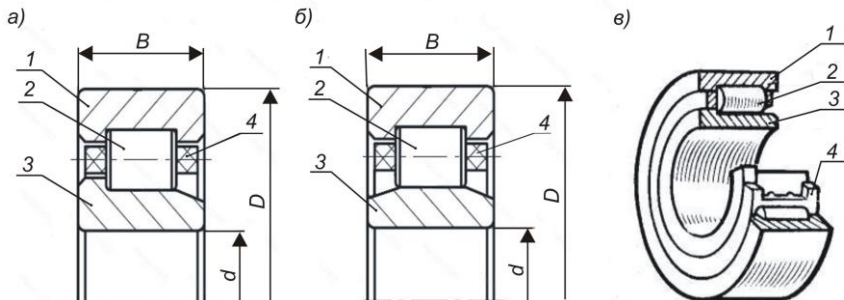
Конструктивное исполнение цилиндрических роликовых подшипников:
